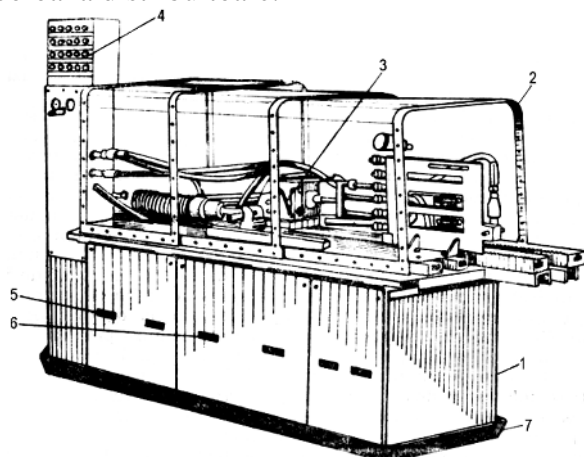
Banc de încercat cilindri și distribuitoare hidraulice BCD-2: 1 – cadru; 2 – apărătoare de protecție; 3 – dispozitive de fixare a subansamblurilor care se încercă; 4 – pupitru electric de comandă și semnalizare; 5 – cilindru hidraulic; 6 – rezervor și filtre; 7 – tavă pentru colectarea scurgerilor de ulei
